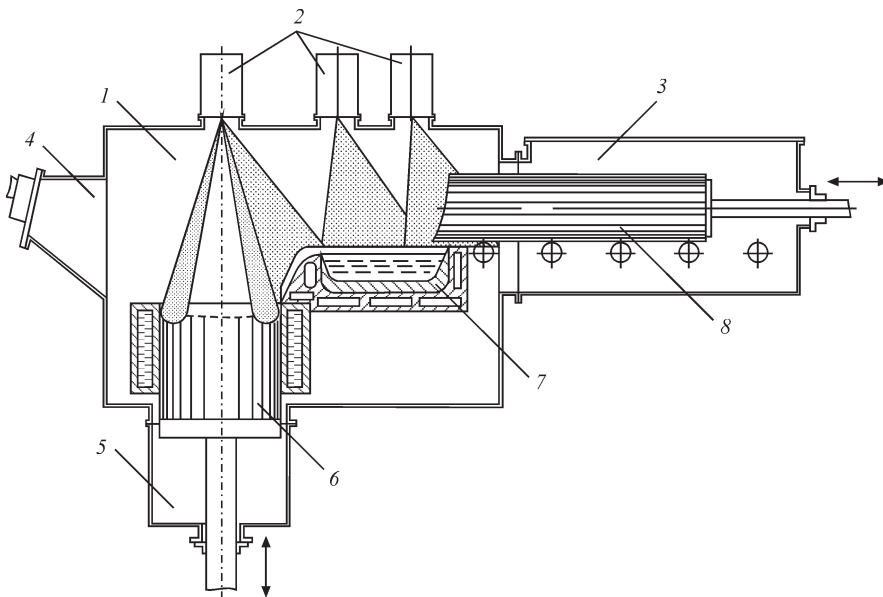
Схема установки UE-5810: 1 — камера плавки; 2 — електронні гармати; 3 — камера заготовки; 4 — оглядова система; 5 — камера зливки; 6 — зливоч; 7 — проміжна ємність; 8 — шихтова заготовка
